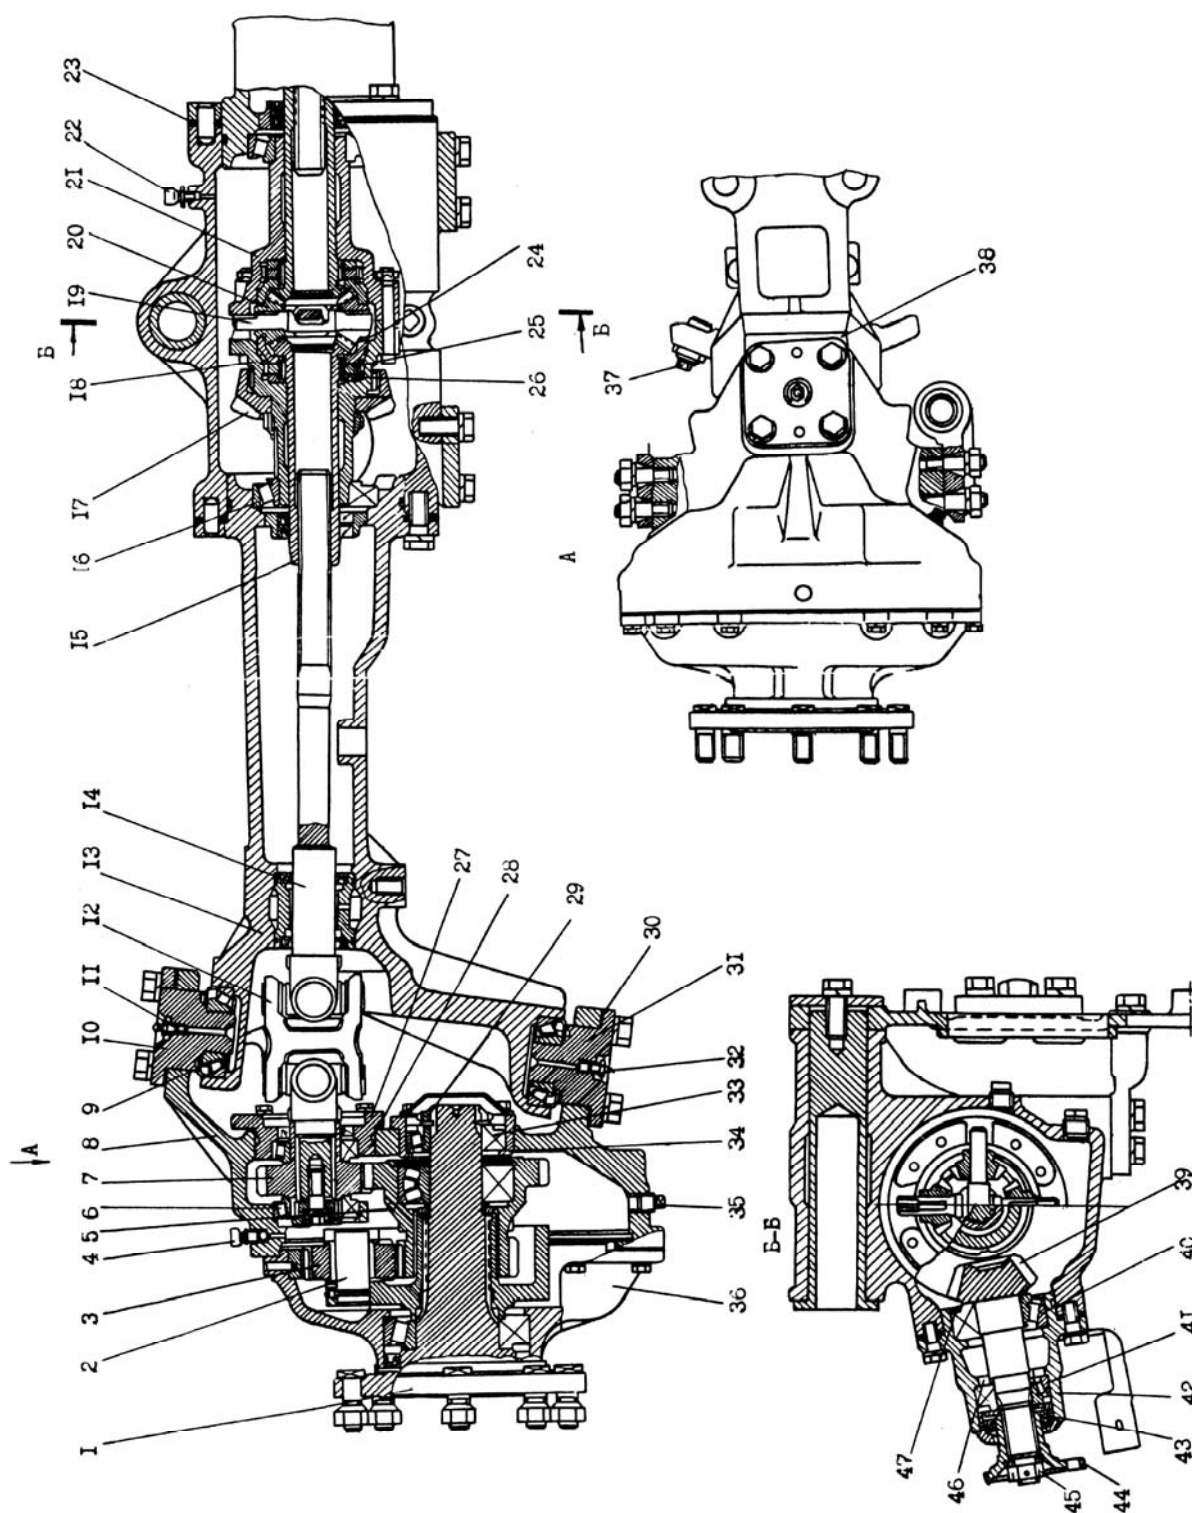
Регулировка подшипников переднего ведущего моста
